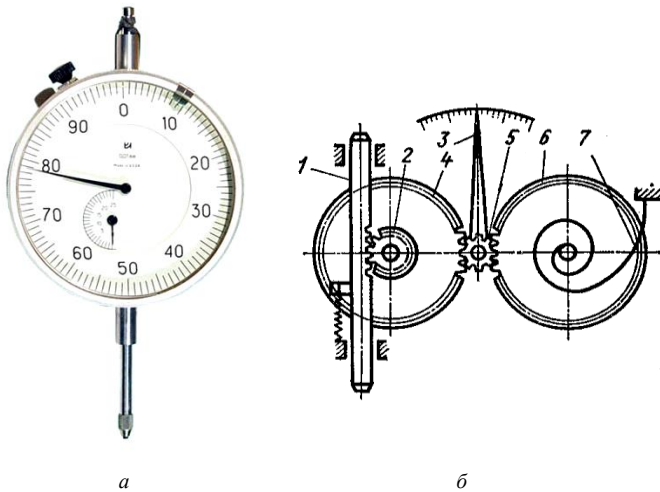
Индикатор часового типа: *а* – общий вид; *б* – кинематическая схема: 1 – измерительный стержень; 2 – зубчатое колесо на 16 зубьев; 3 – большая стрелка индикатора; 4, 6 – зубчатое колесо на 100 зубьев; 5 – зубчатое колесо на 10 зубьев; 7 – спиральная пружина
